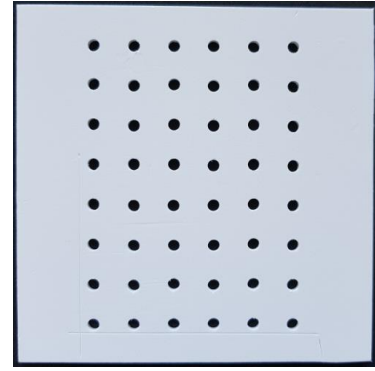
Foto de placa (90 mm X 90 mm) de furos de 3 mm
